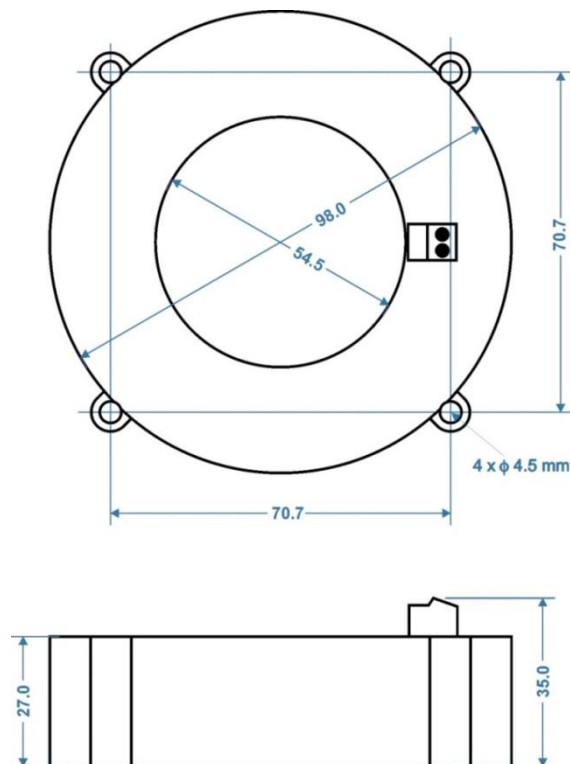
Корпус CR 05-55, CR 1-55, CR2-55
